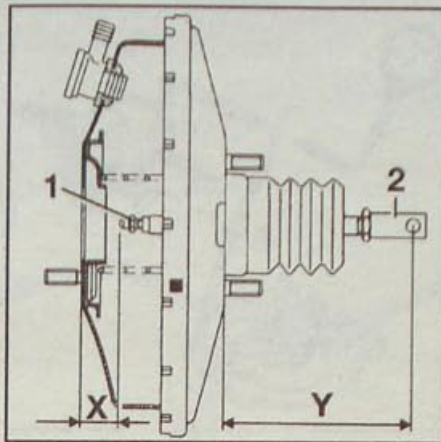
Места проверки размеров перед установкой вакуумного усилителя тормозов:
